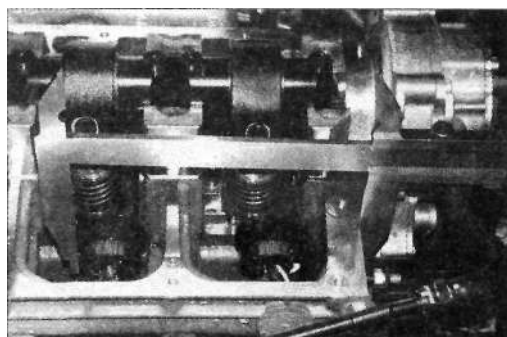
Коррекция положения насос-форсунки в головке блока цилиндров при помощи штангенциркуля
